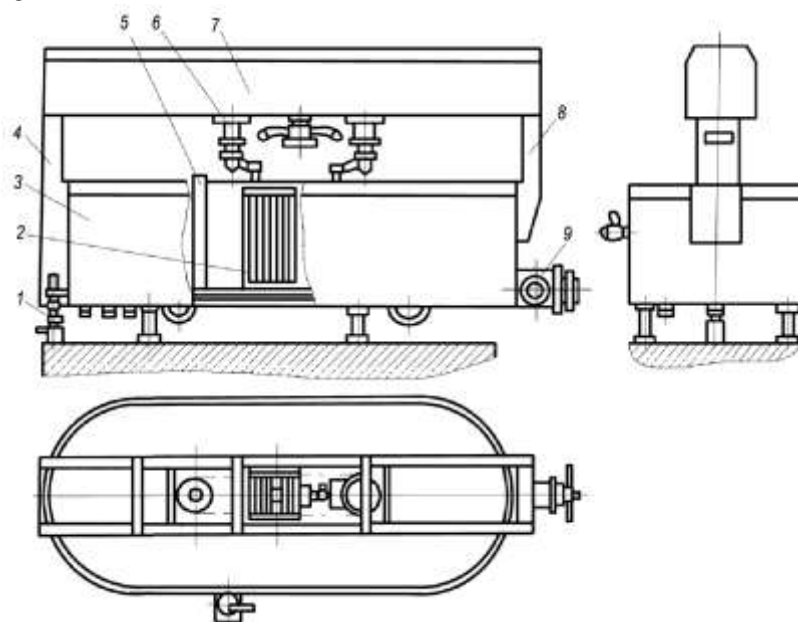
Схема ванни для виготовлення сирного зерна:
